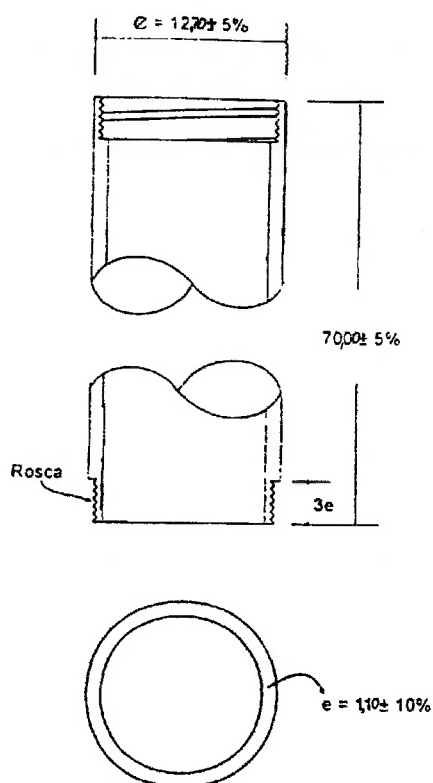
Dimensões do segmento metálico (unidades em cm).
